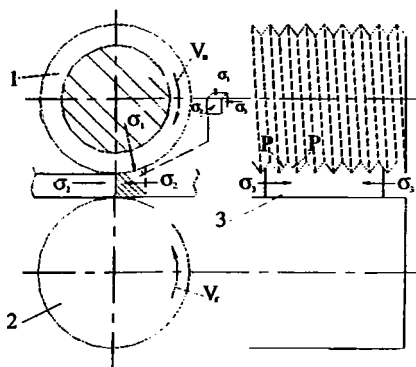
Схема кинематического и напряженного состояния: 1 - рифленый валок; 2 - гладкий валок; 3 - полоса
